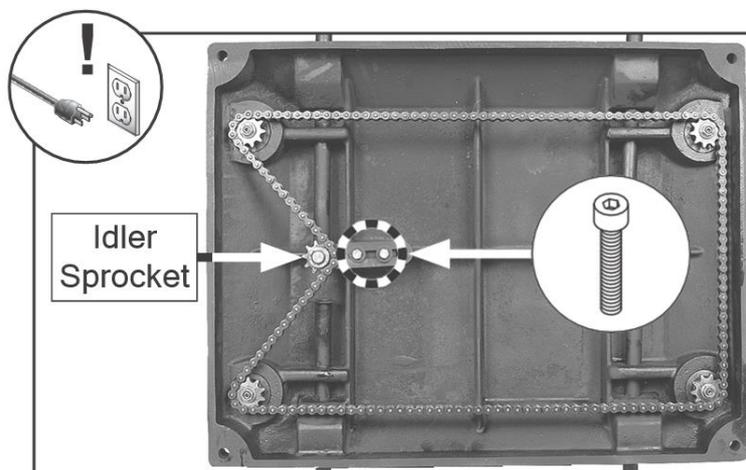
Расположение направляющей звездочки и стопорных винтов.
